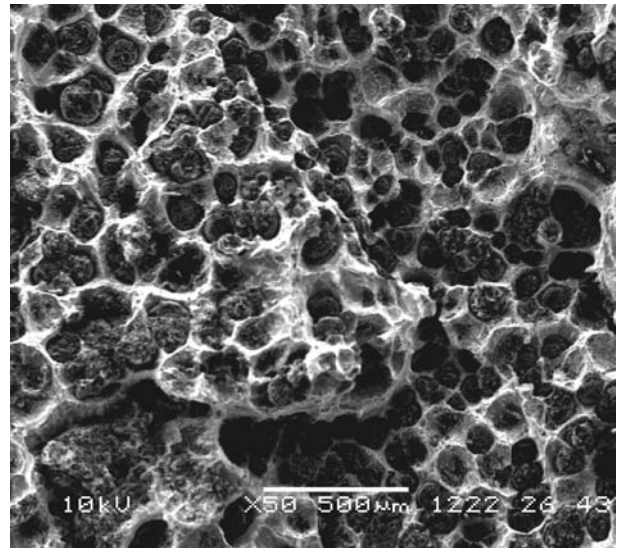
Superficie de fractura del ensayo de K_{IC} de la probeta 3A, mecanizada del centro térmico del cubo de fundición.
